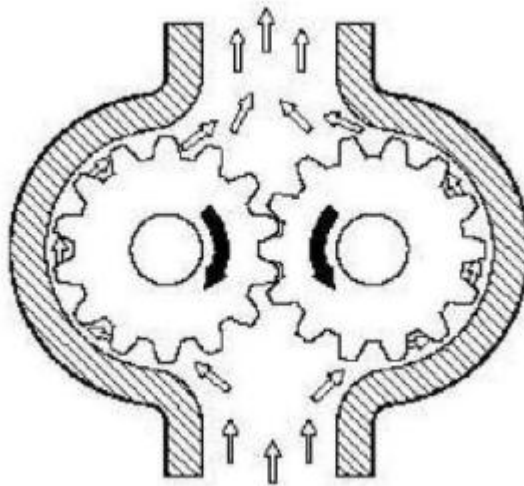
Micro pompe rotatif à double engrenage [9].
